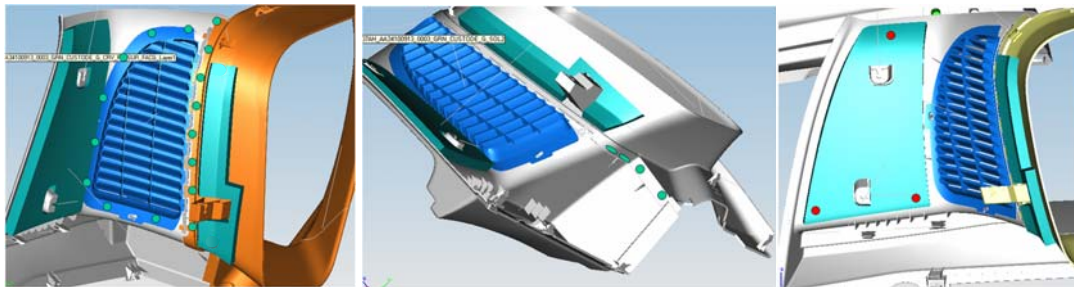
Ultrazvukové svařovací zařízení se založenými komponenty CD sloupku [34]
